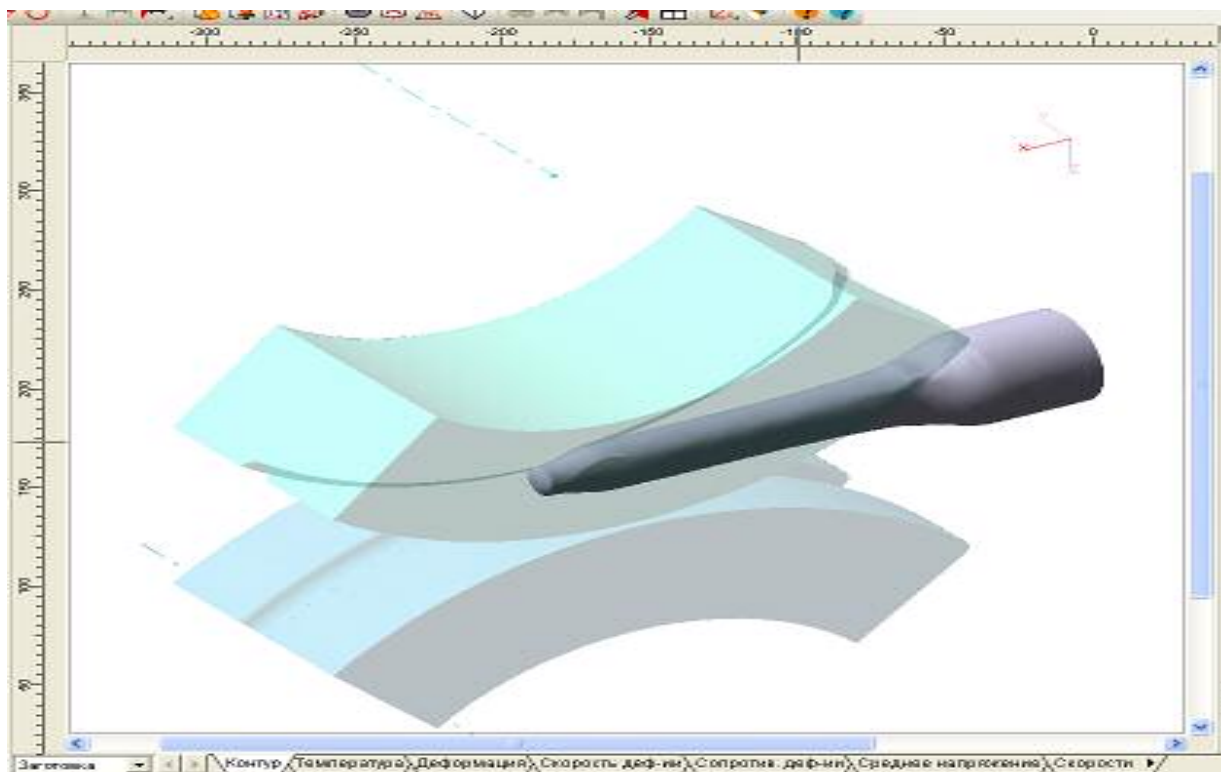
Заготовка после 4 прохода (последнего) вальцовки .Вид с инструментами.
